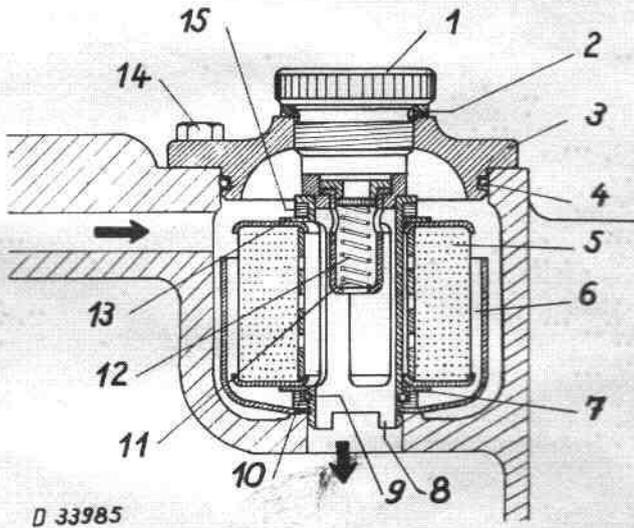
Coupe du filtre à huile de l'hydraulique
